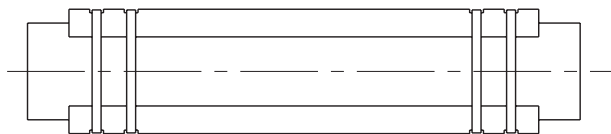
Utforming av gummipolstring – gummi skal være 50 Durometer
